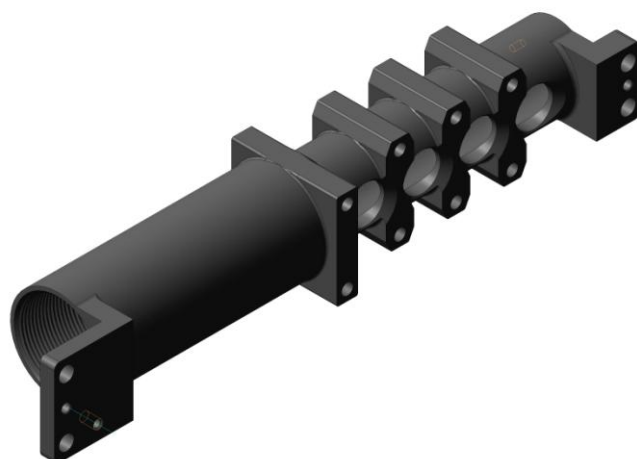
Общий вид детали «Корпус коллектора распределительного»
